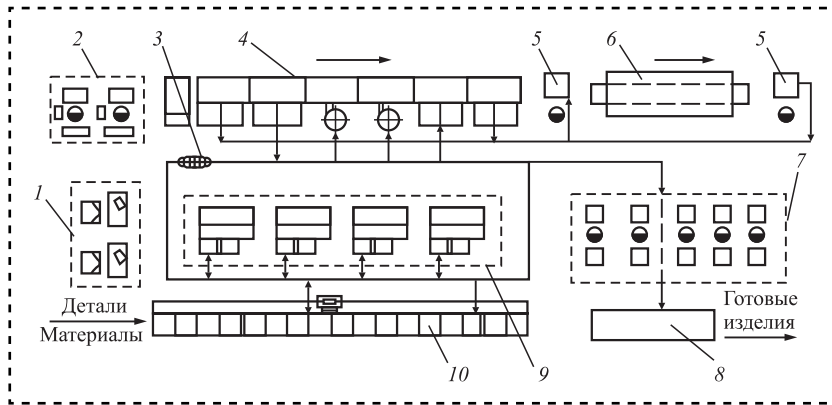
Линия сборки керамического корпуса ИМС со штырьковыми выводами и установки полупроводникового кристалла:
